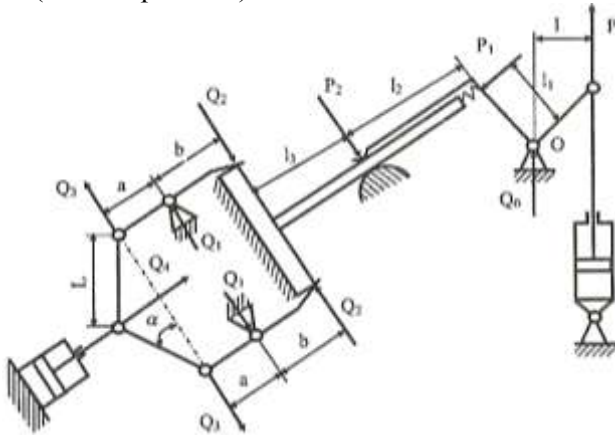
Розрахункова схема важільного затискового пристрою кондуктора-кантувача [4]
